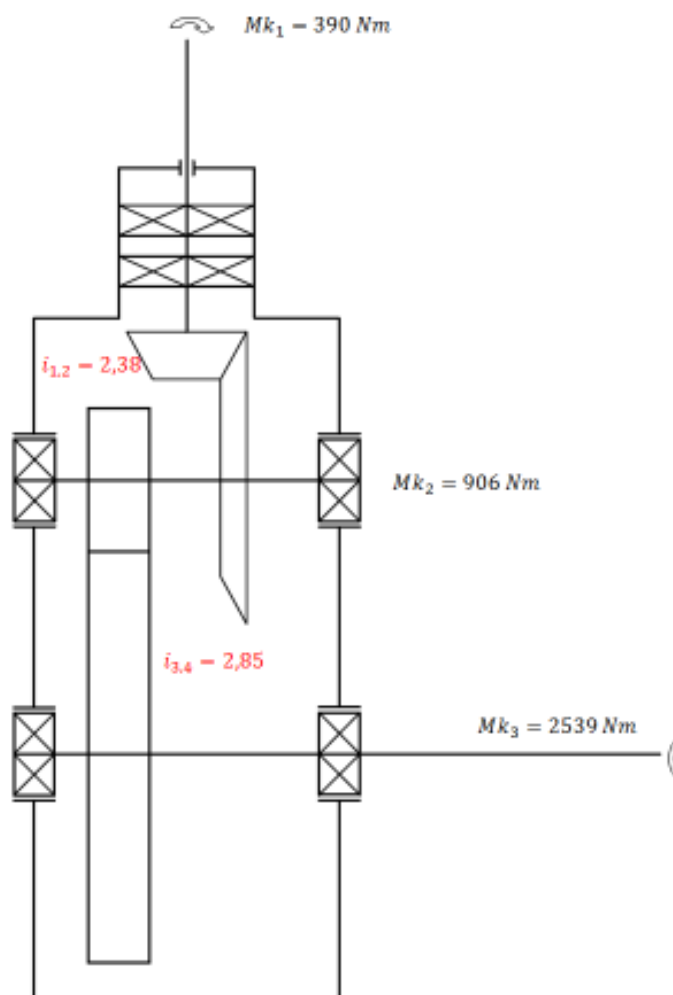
Převodová skříň pevně spojená s motorem[13]
